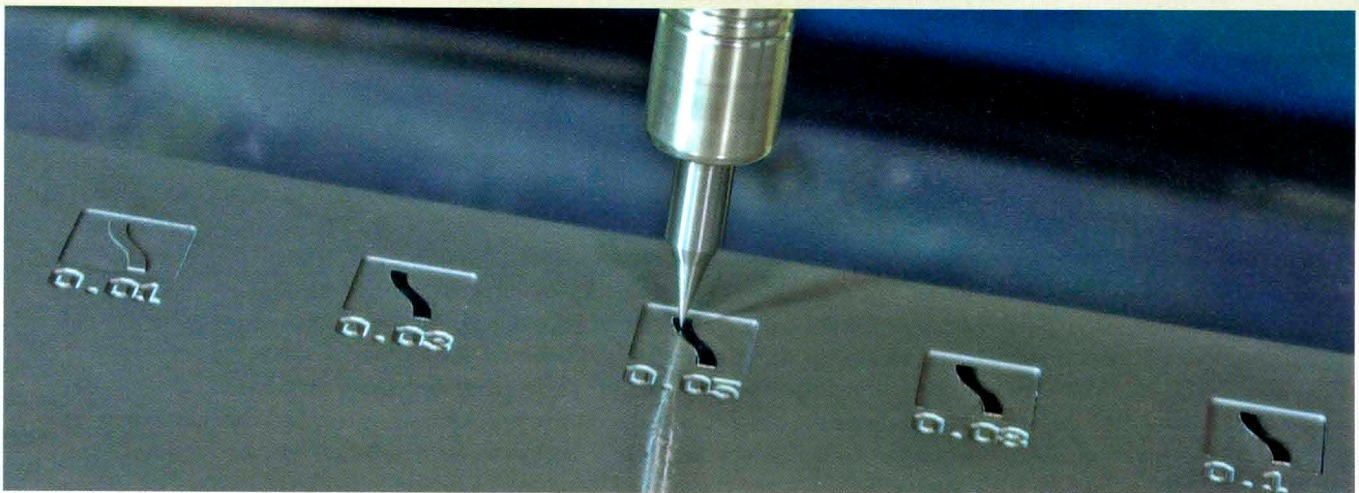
Fräsen am Limit: Für ein Spritzguss-Projekt in Mikrodimensionen vergleicht Mitec die Fräsergebnisse unterschiedlicher Fräser mit Schneidendurchmessern zwischen 0,1 und 0,03 mm. Zerspannt wird dabei Werkzeugstahl mit einer Härte von 58 HRC
